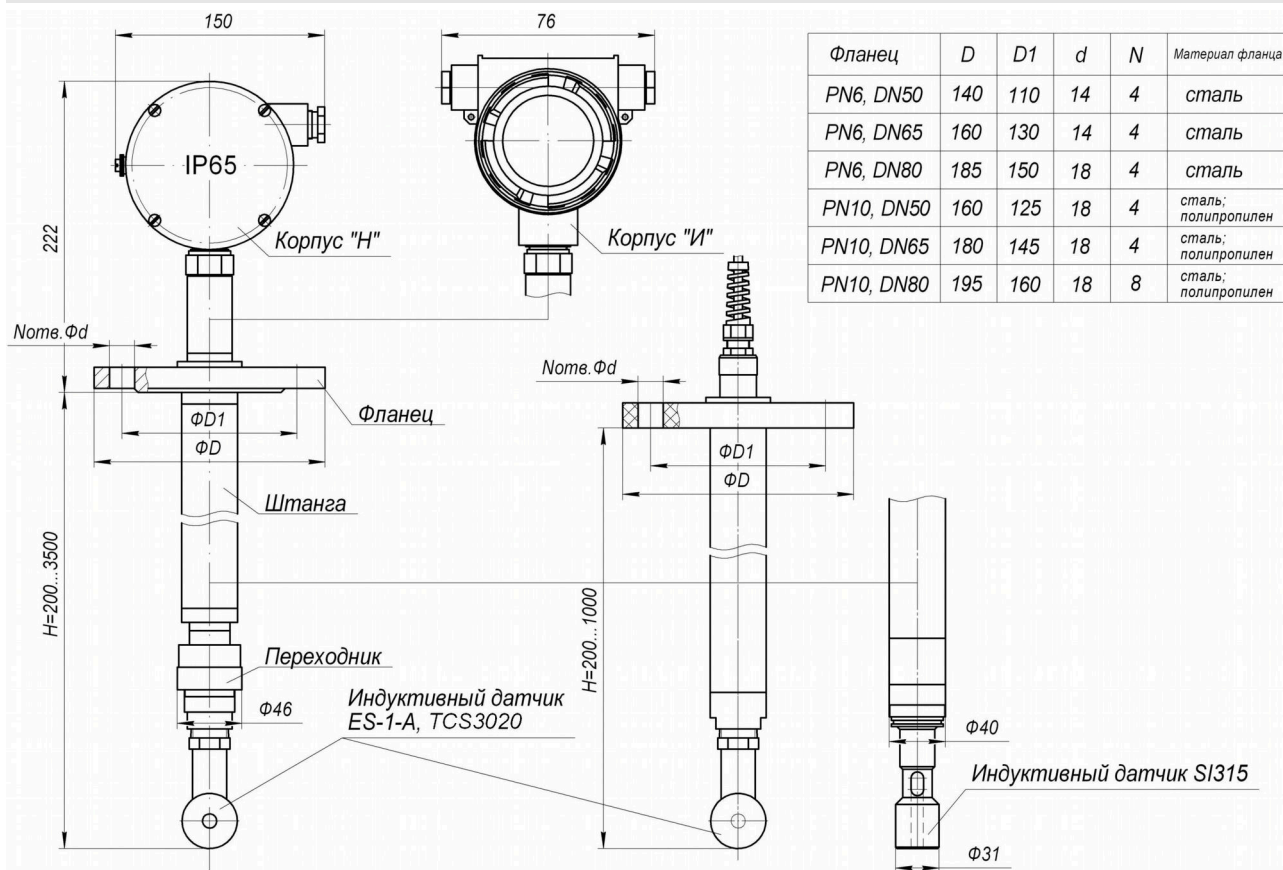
Габаритные и монтажные размеры первичного преобразователя с индуктивными датчиками ES-1-A, TCS3020, SI 315
